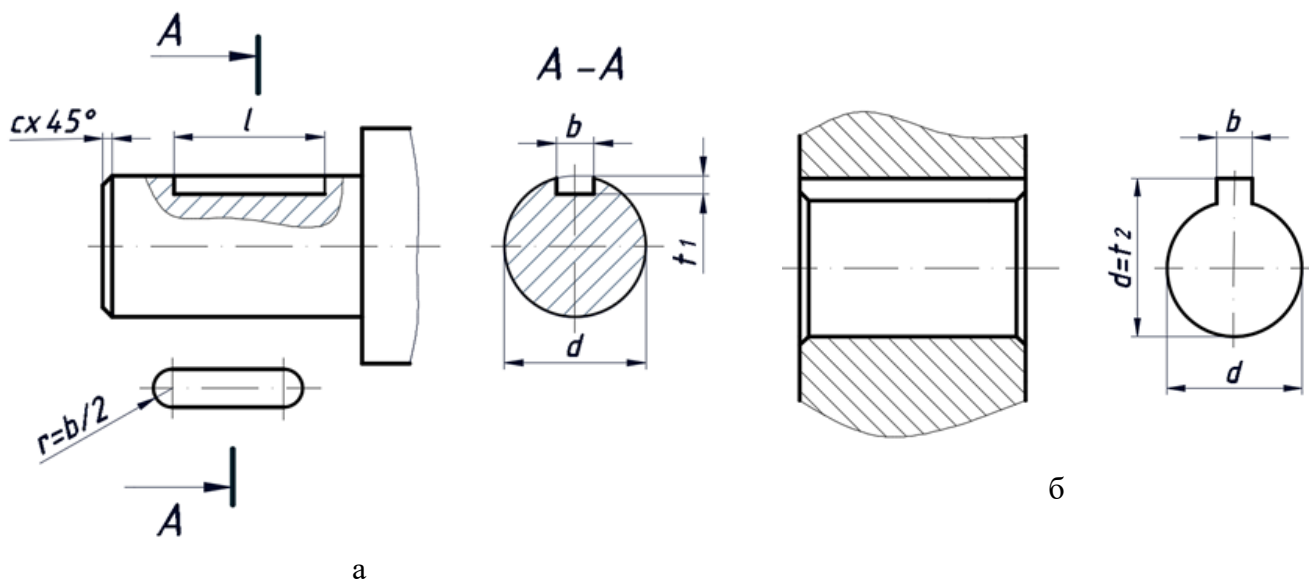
Образец изображения шпоночных пазов: а- на валу, б - ступице колеса.
